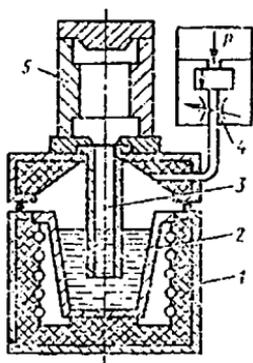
Схема установки для литья под низким давлением: 1 — тигельная печь сопротивления; 2 — тигель; 3 — металлопровод; 4 — прибор; 5 — кокиль
